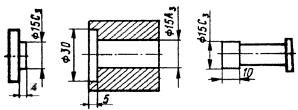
Разъемная форма для получения заготовки аншлифа
